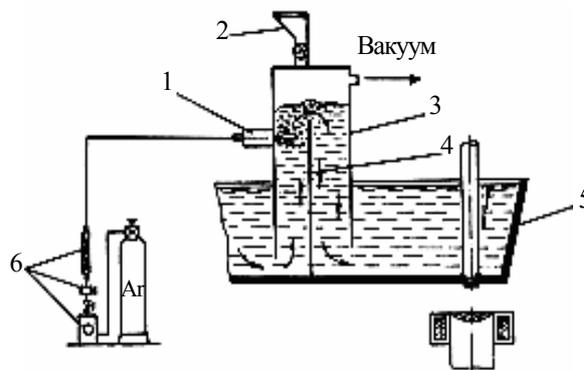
Схема вакуумно-плазменной обработки сплавов при непрерывной разливке металла:
